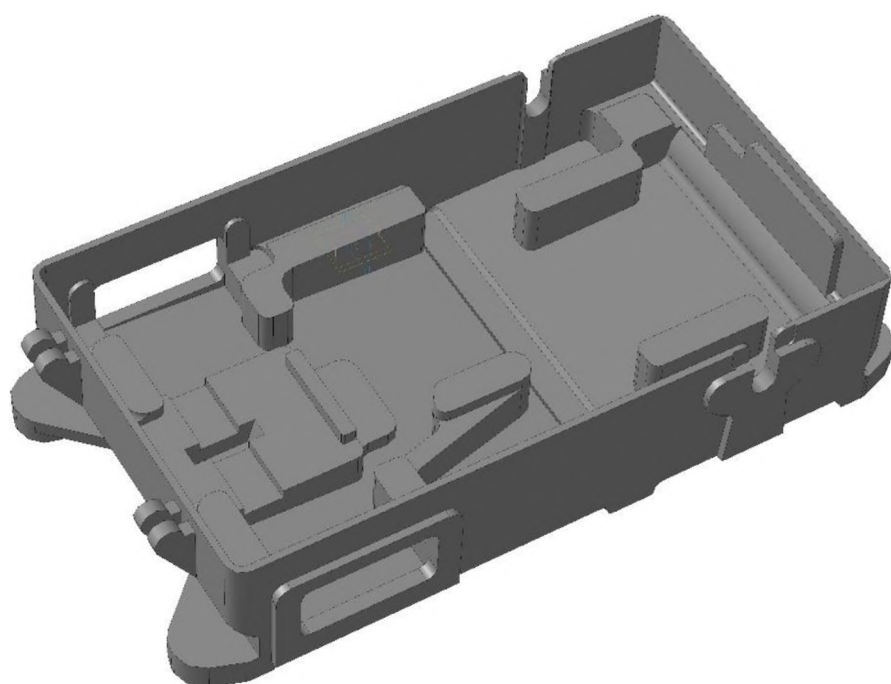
3D модель деталі «Корпус». Ізометрія, вигляд зверху
